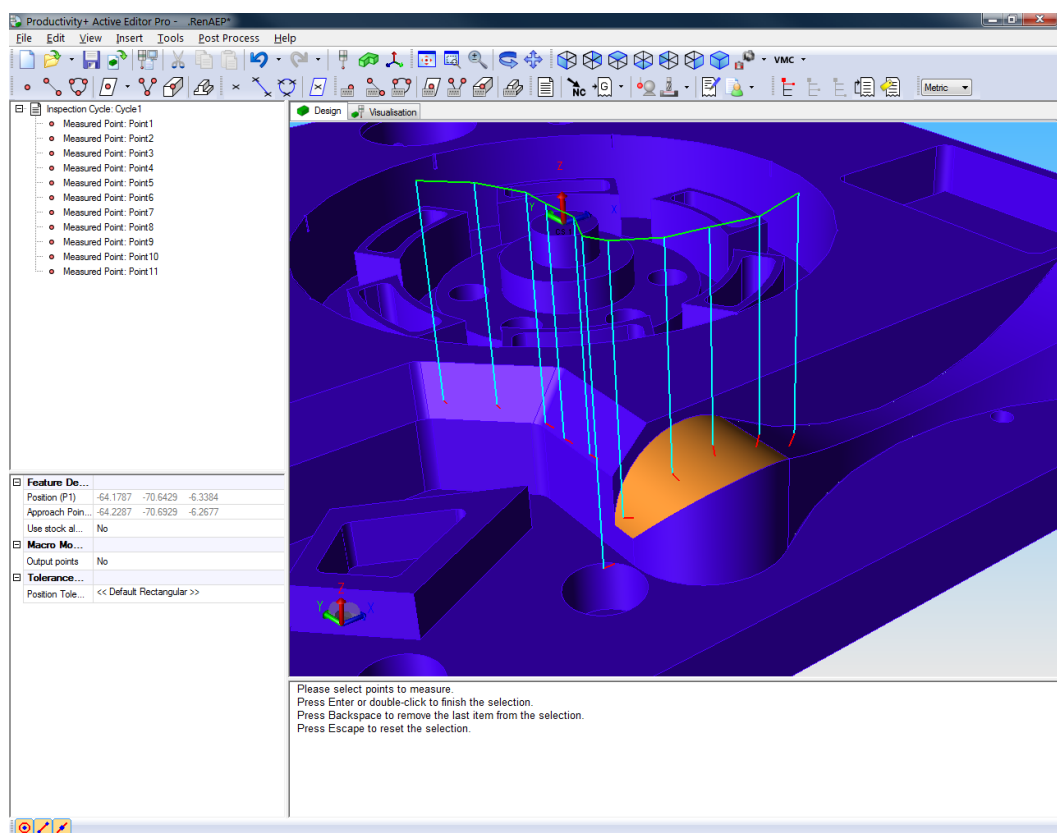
Ustavení obrobku podle kruhové geometrie (20)
